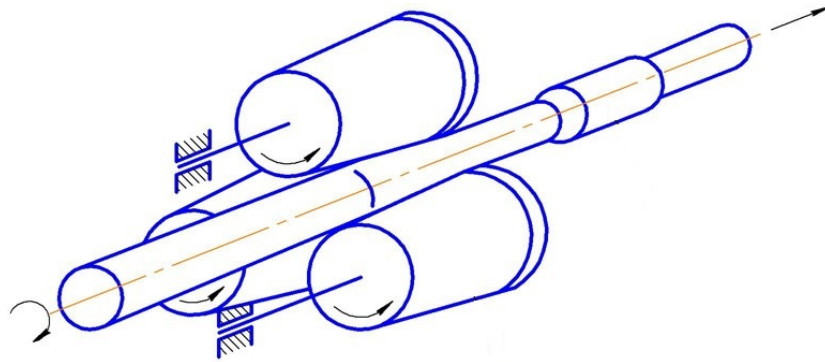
Схема поперечно-винтовой прокатки
